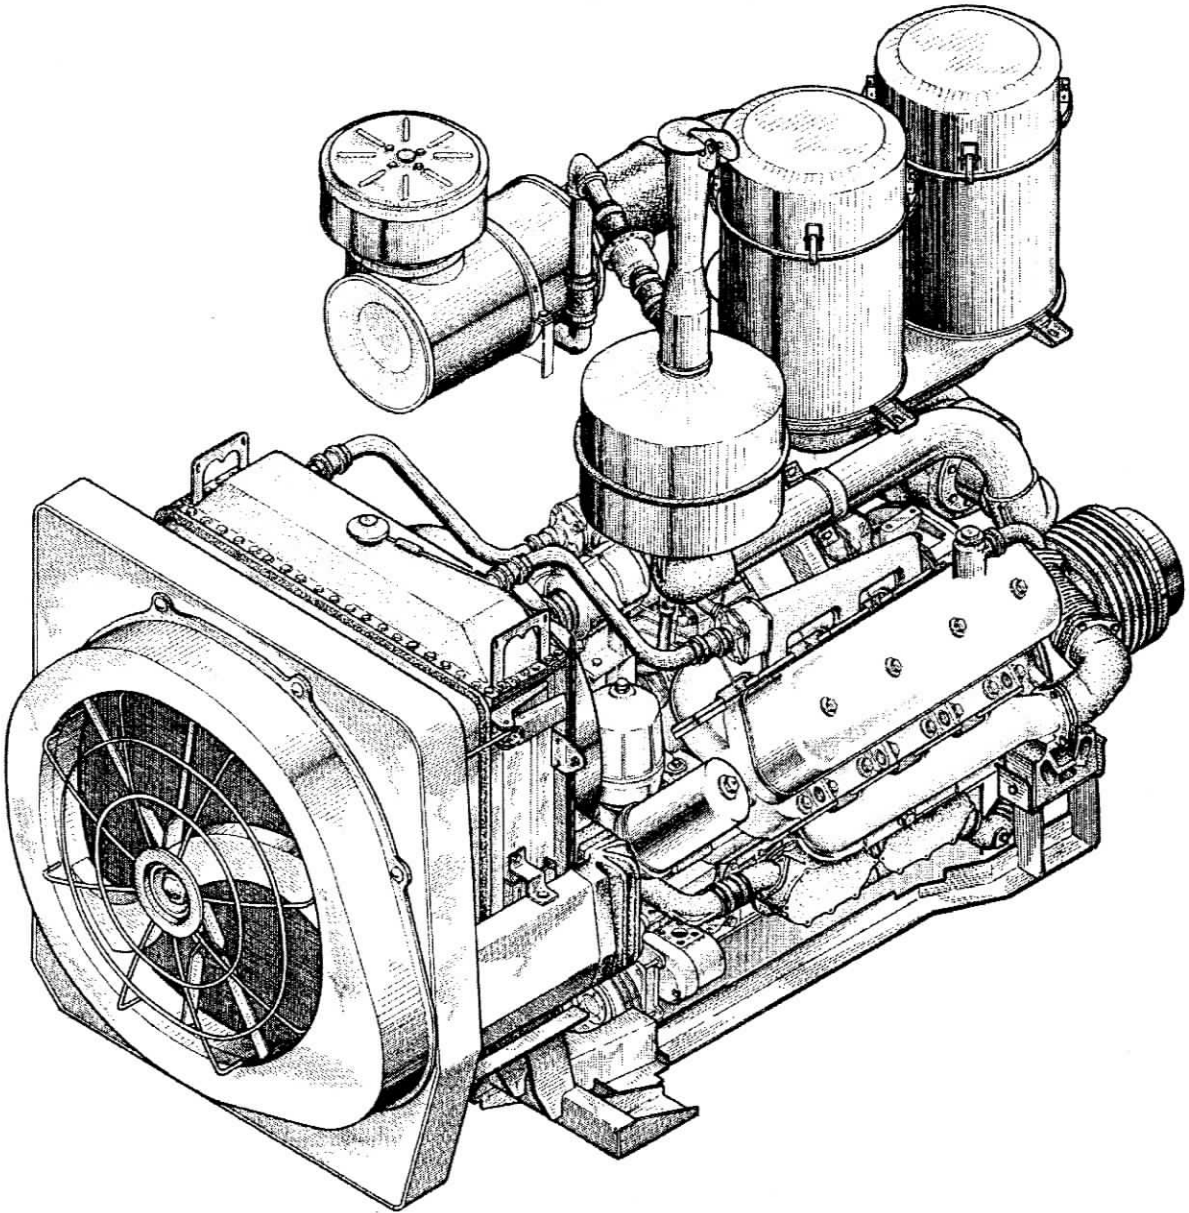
а - Установка моторная с двигателем ЯМЗ-238ДК-1.
